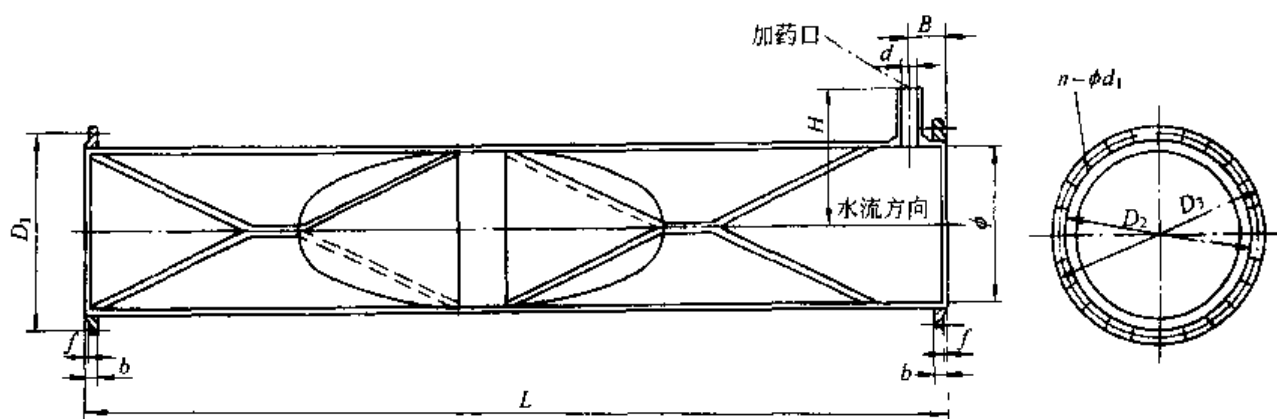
GJH 型管式静态混合器外形及安装尺寸
